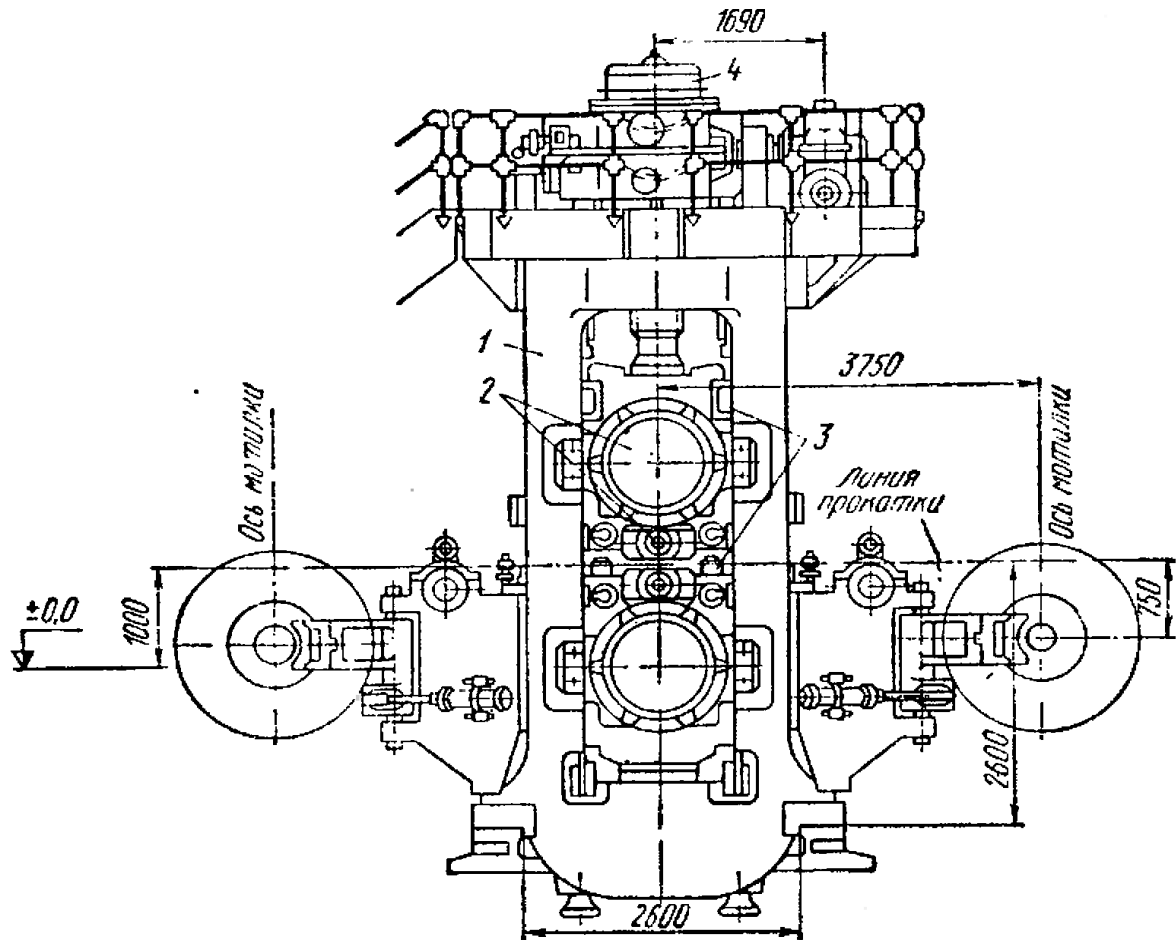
Загальний вид чотирьох валкову кліті
